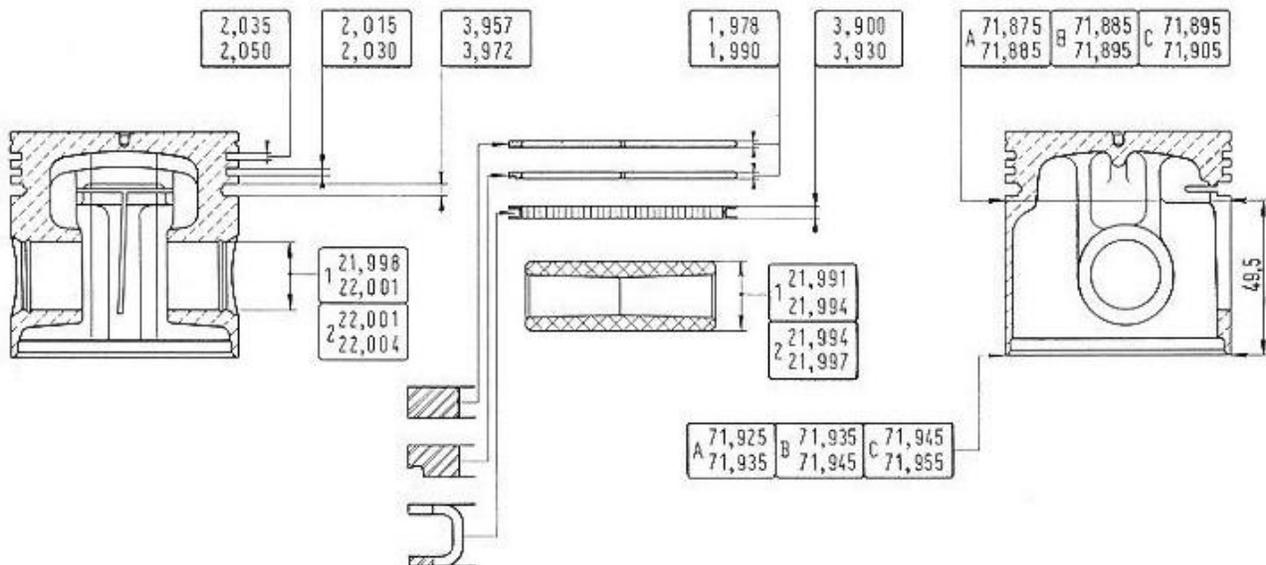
Wichtigste Daten für die Kolben, die Kolbenbolzen und die Kolbenringe.
